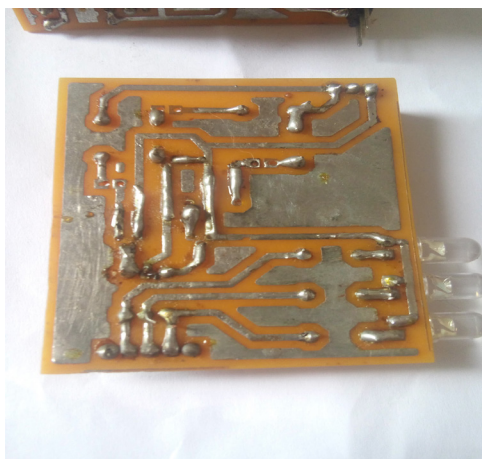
PCB Confeccionada através do método de termotransferência com os componentes soldados. Autoria Própria.
